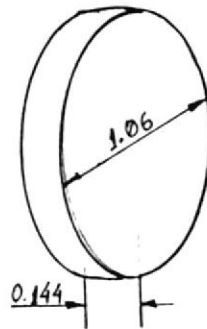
Dimensiones de un cilindro semejante a la voluta del ventilador
